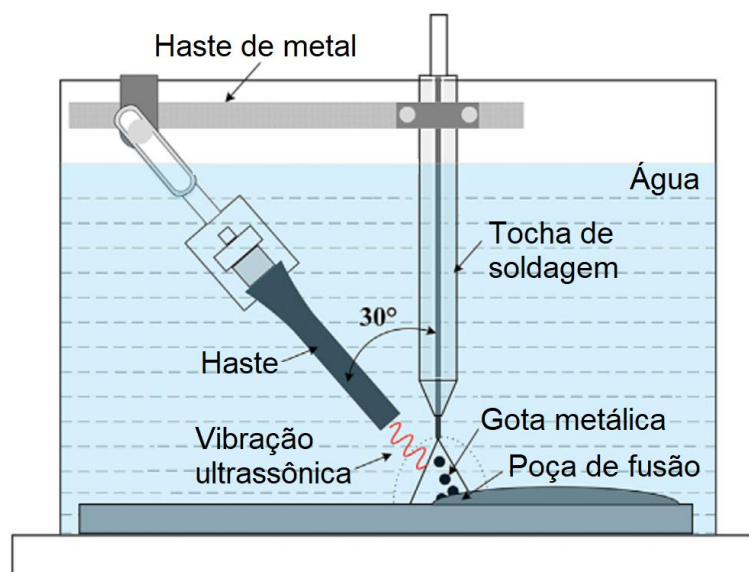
Esquema de montagem do cabeçote de ondas ultrassônicas inclinado em relação à tocha de soldagem.
